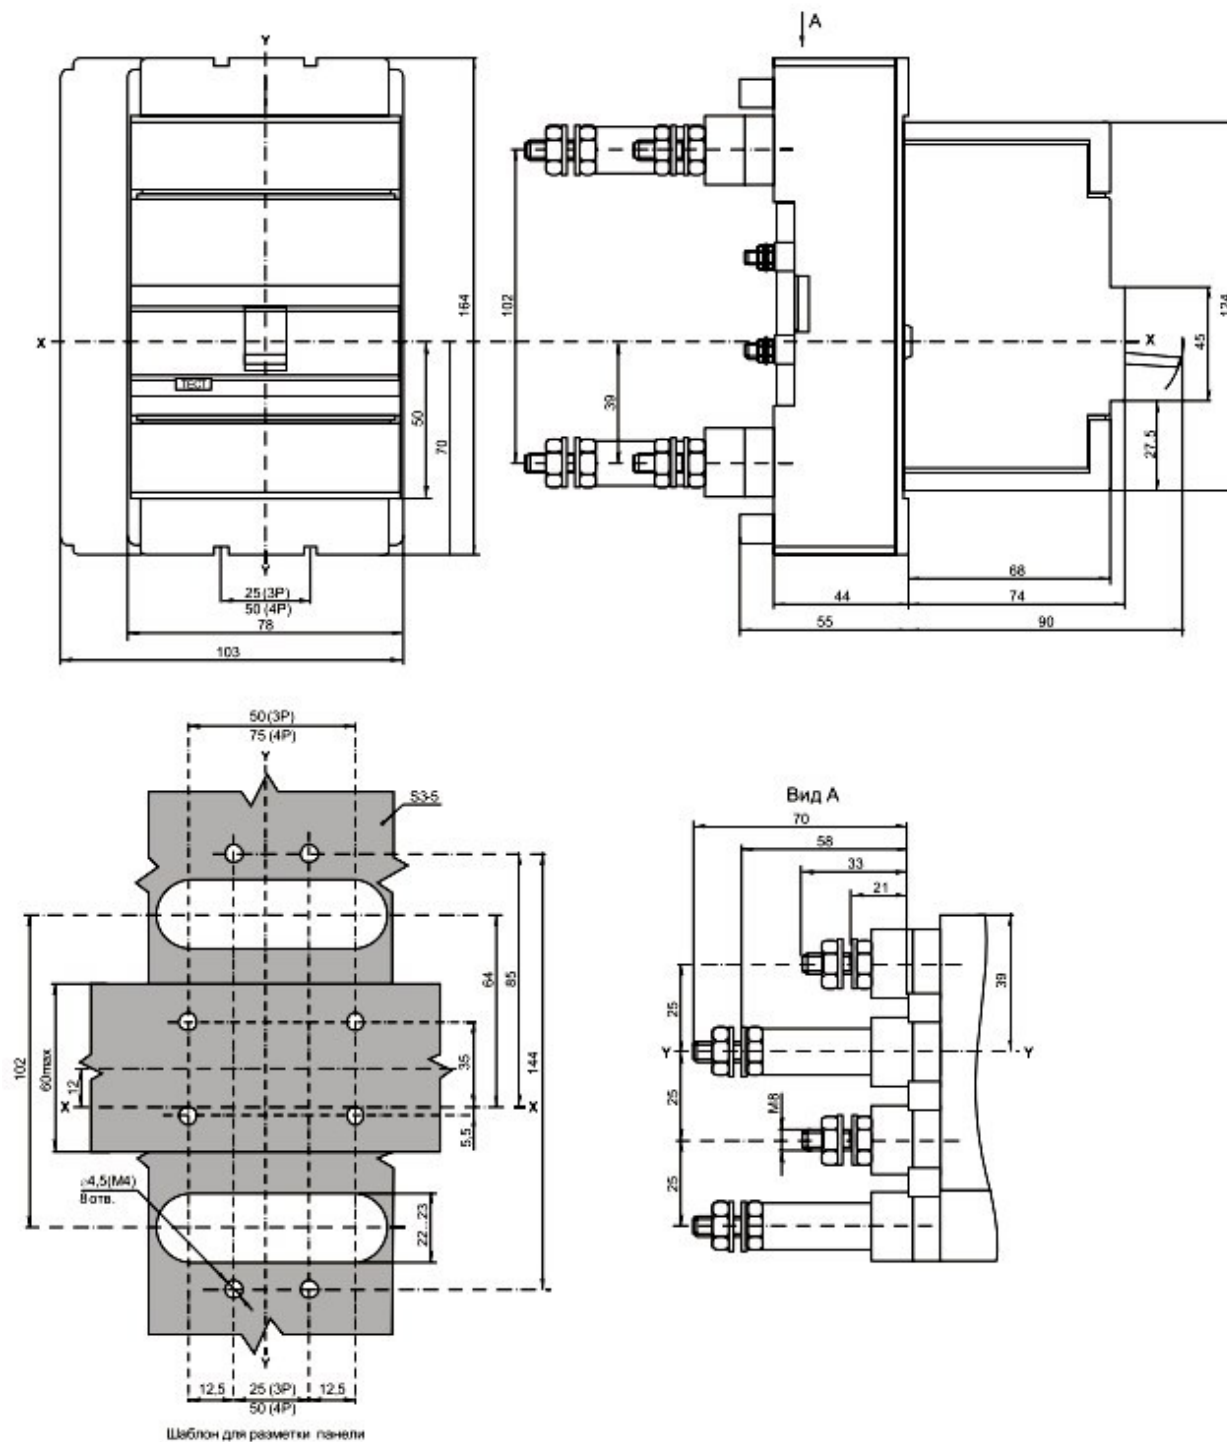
Габаритные, установочные и присоединительные размеры выключателя ВА88-32 при преобразовании его во втычное исполнение с
